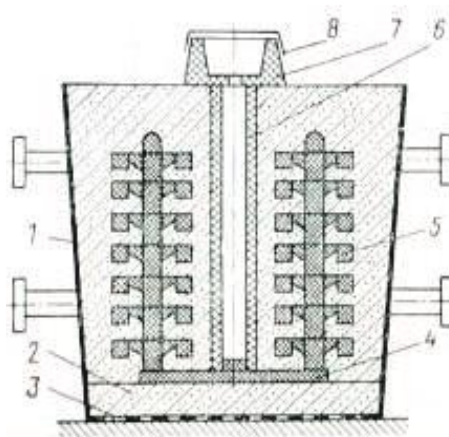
Литейные опоки-контейнера (стенки с отверстиями): 1-стенки; 2-постель из жсс; 3-дно; 4-модель литника; 5-модель отливки; 6-керамический стояк; 7-чаша; 8-крышка
